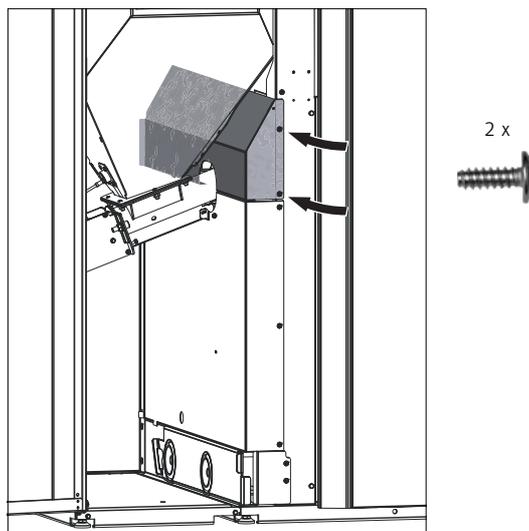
Spingere la piastra di protezione dal contatto dietro e avvitarela anteriormente
